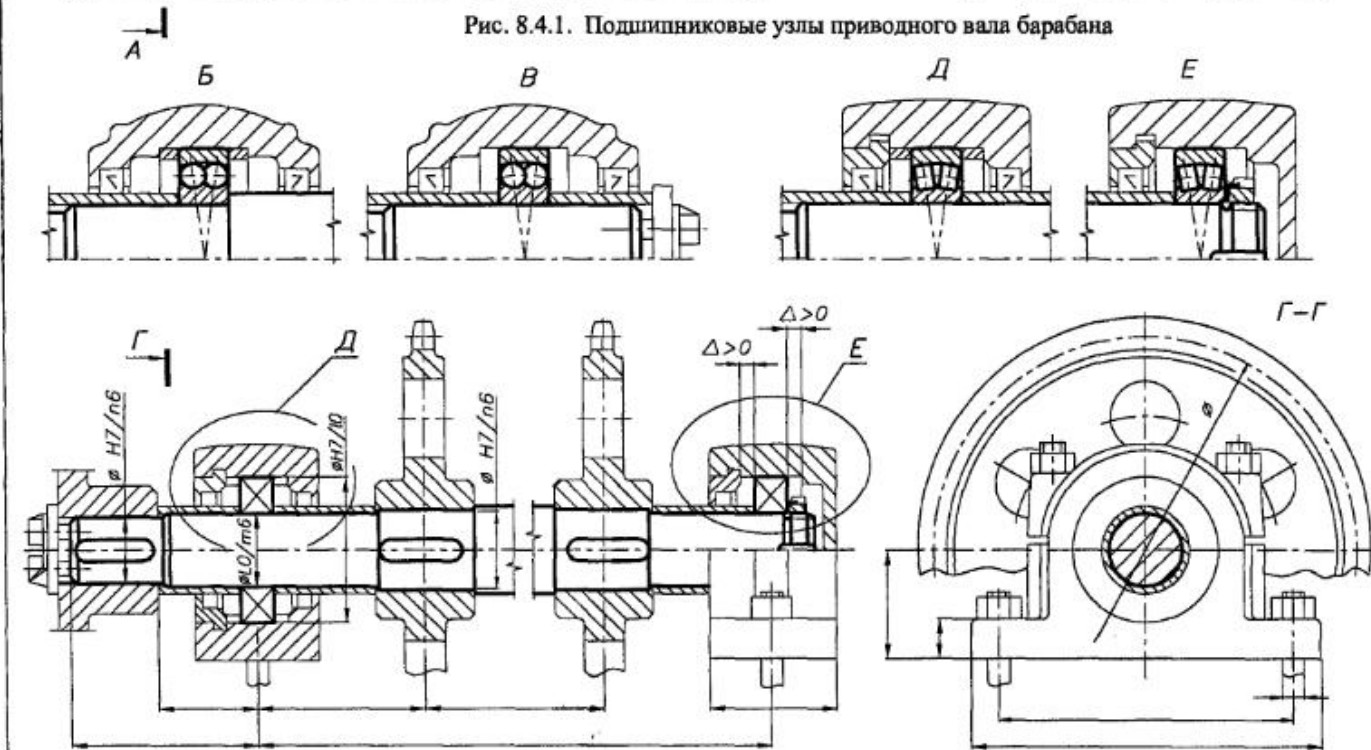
Подшипниковые узлы приводного вала звездочек
